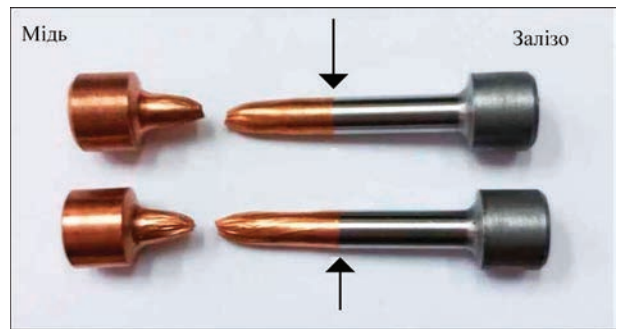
Вигляд зразків біметалічної сполуки сталь-мідь після випробування на розрив
